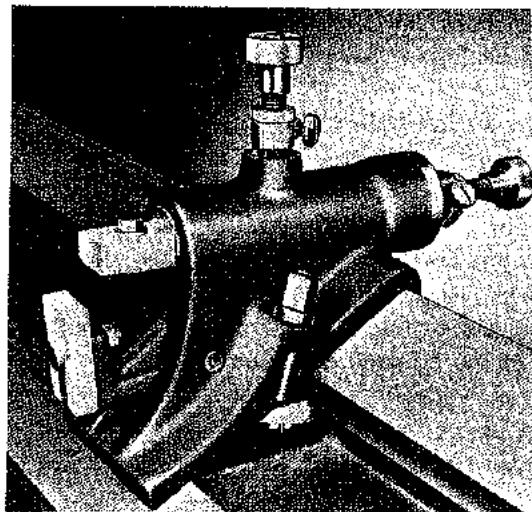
Luneta de respaldo (Cincinnati Milling Machine Co.)
